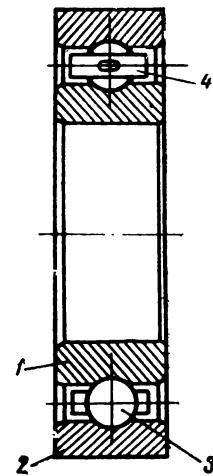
Радиальный однорядный шариковый подшипник в разрезе:
